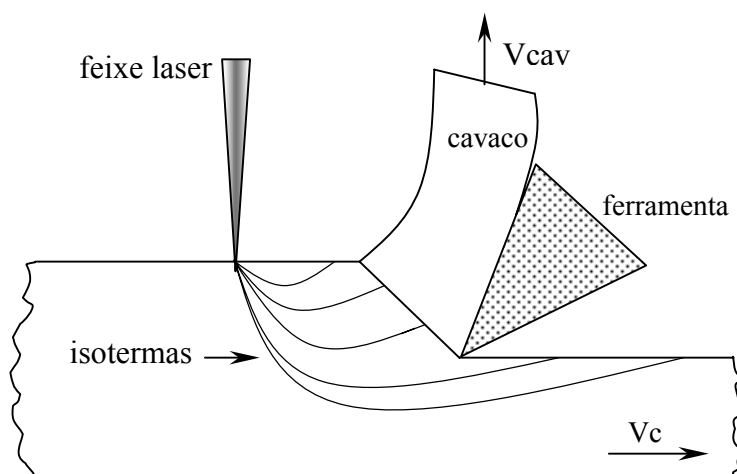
Princípio da usinagem a quente assistida por laser (SALEM et al., 1995).
